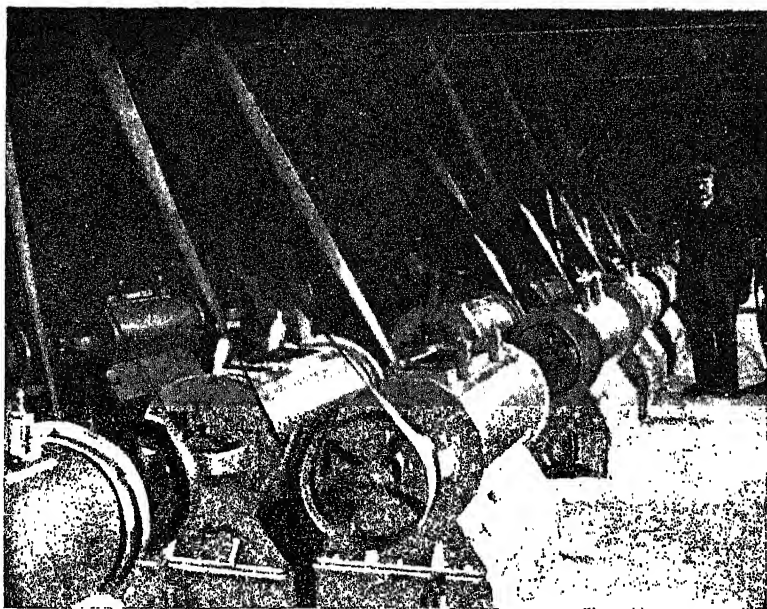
Vue d'ensemble d'une salle de machines à polir la poudre d'aluminium.
